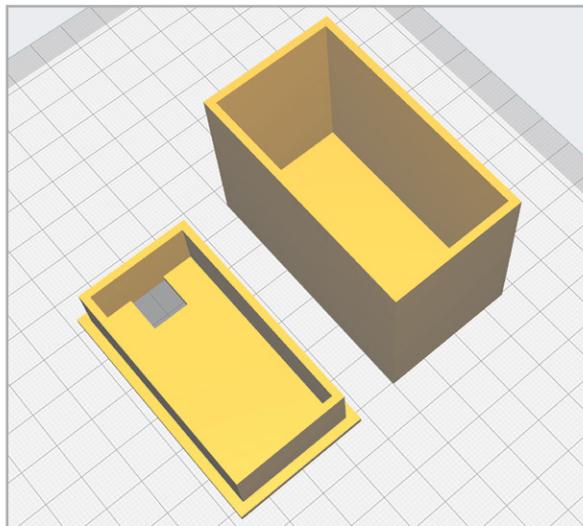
In OpenSCAD konstruiertes Gehäuse für den Pegelmesser - Ansicht im Slicer
